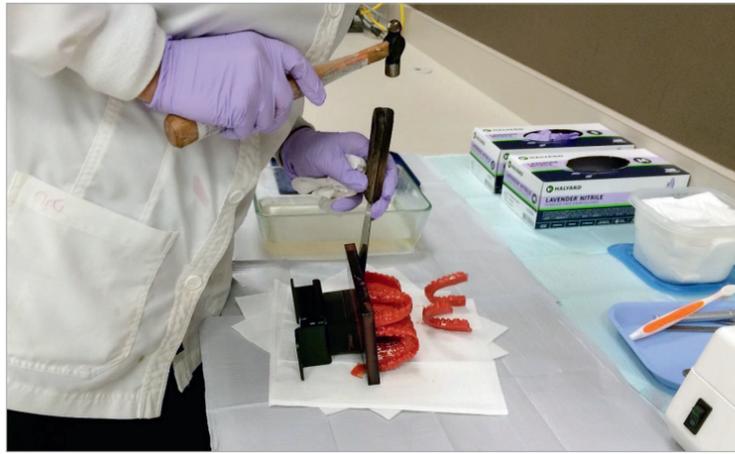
Entfernen der gedruckten Zahnkränze von der Aufbauplattform durch einen Labortechniker. – Abb. 6: Auf einem EnvisionTEC Perfactory Vida wurden diese Zahnkränze aus Ortho Tough, einem haltbaren Dentalwerkstoff, gedruckt und gehärtet. (Abb. 2 bis 6: Mit freundlicher Genehmigung der EnvisionTEC GmbH Gladbeck)
